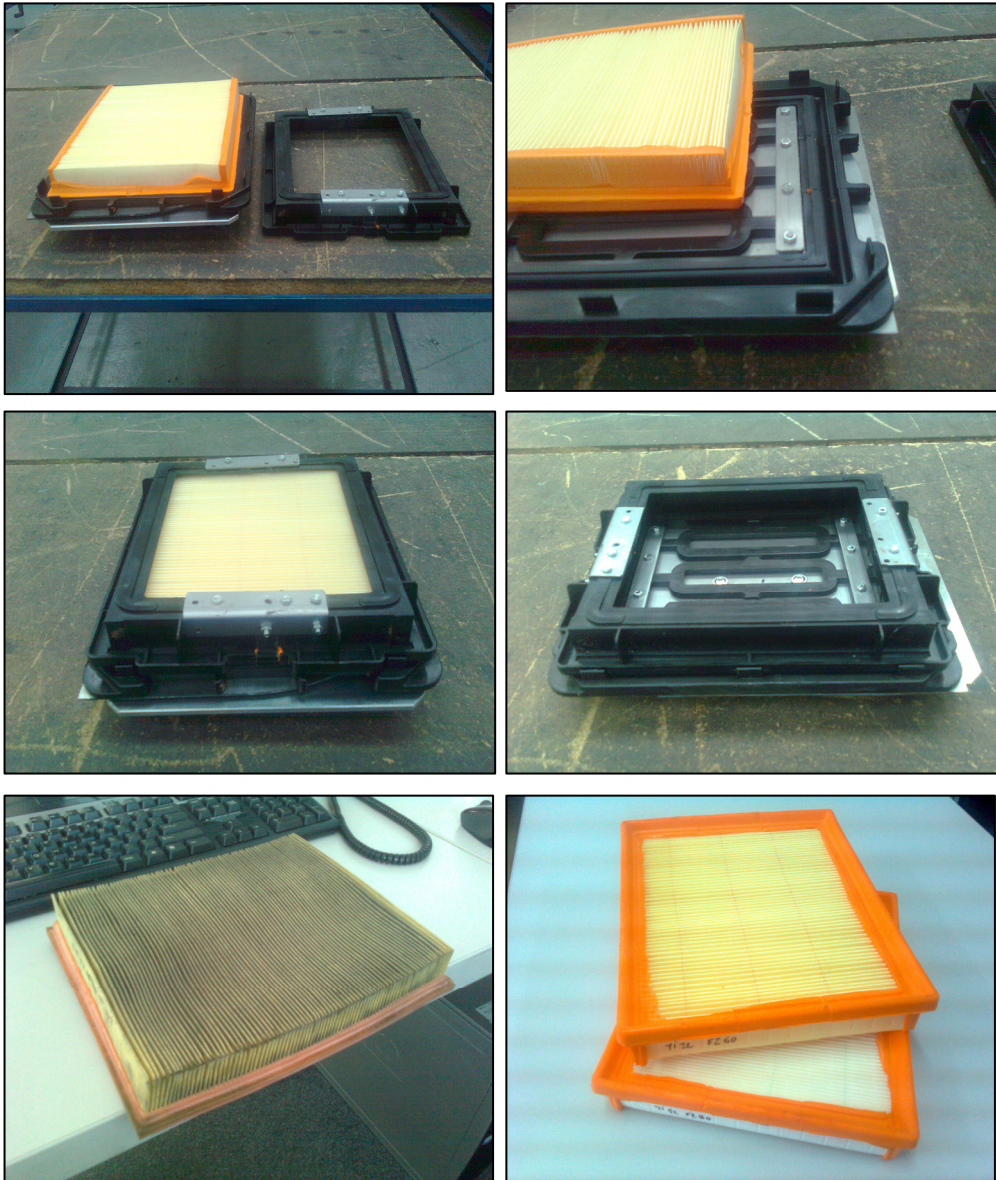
Forma de turnare a elementului construit, elementul original Opel si elemente finalizate
